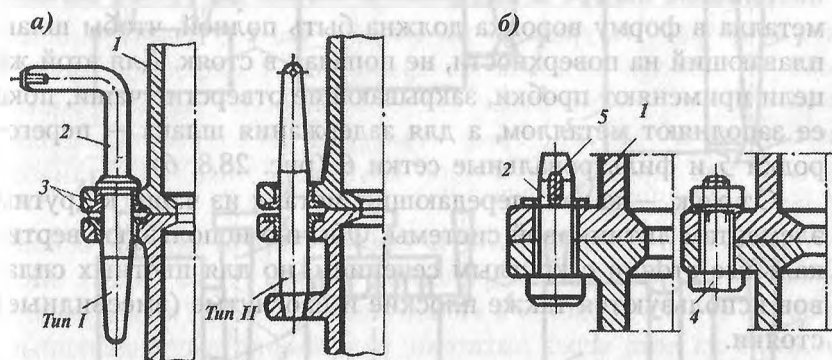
Спаривание (а) и скрепление (б) опок: 1 — опока; 2 — штырь; 3 — втулка; 4 — болт; 5 — клин
